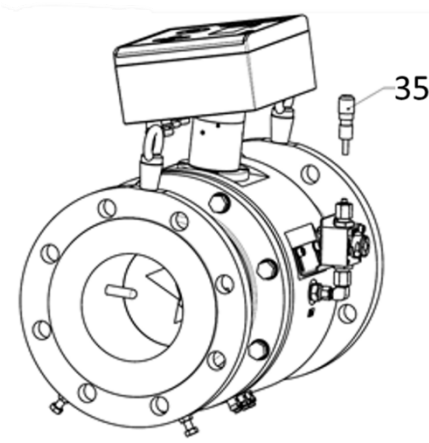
Versione con rubinetto a 3 vie e raccordo Minimesse
